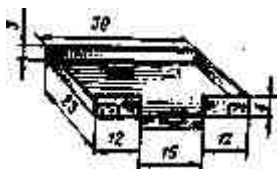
Выдвижная кормушка К. Шломина для нутрий (размеры в см)
